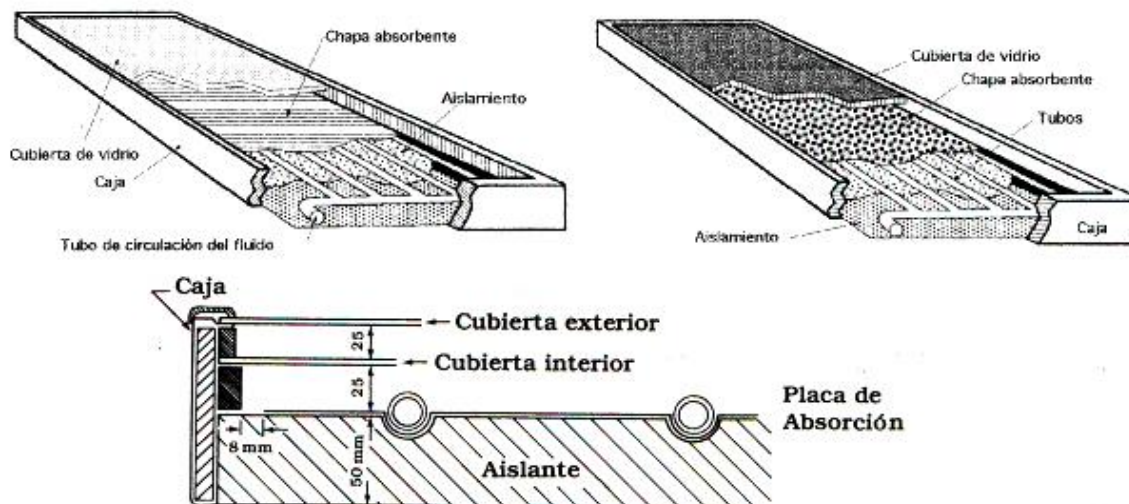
ESTRUCTURA DEL COLECTOR Y CORTE TRANSVERSAL CON 2 CUBIERTAS DE VIDRIO.
